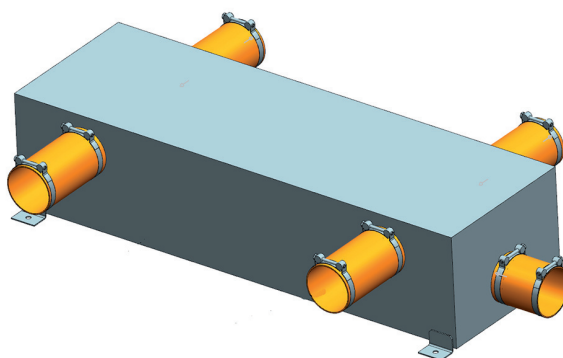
Воздушный коллектор для отопления двух батарейных блоков
